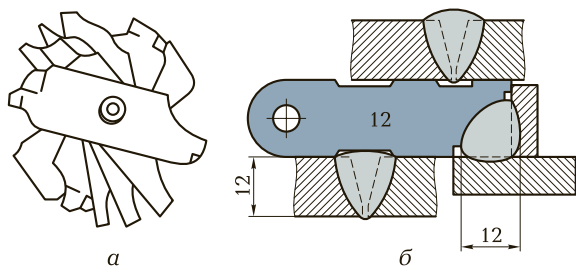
Универсальный шаблон для контроля угловых швов (а) и использование специального шаблона для контроля сварных швов (б)
